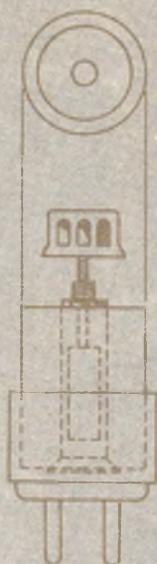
Particolari di montaggio delle bobine intercambiabili.
